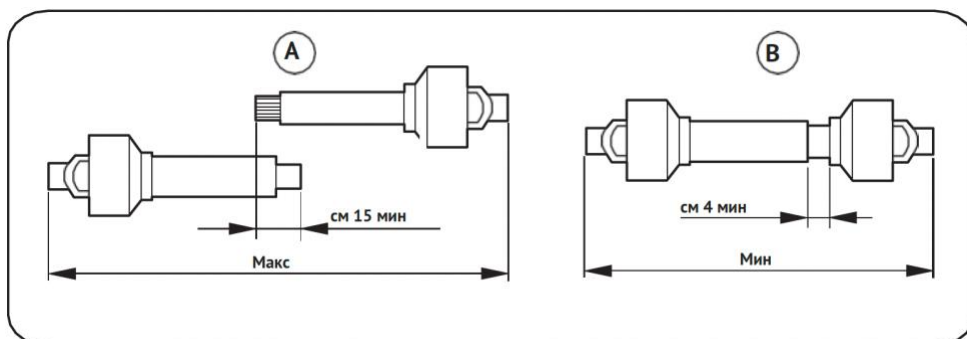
Перекрытие труб карданного вала и монтажный зазор
